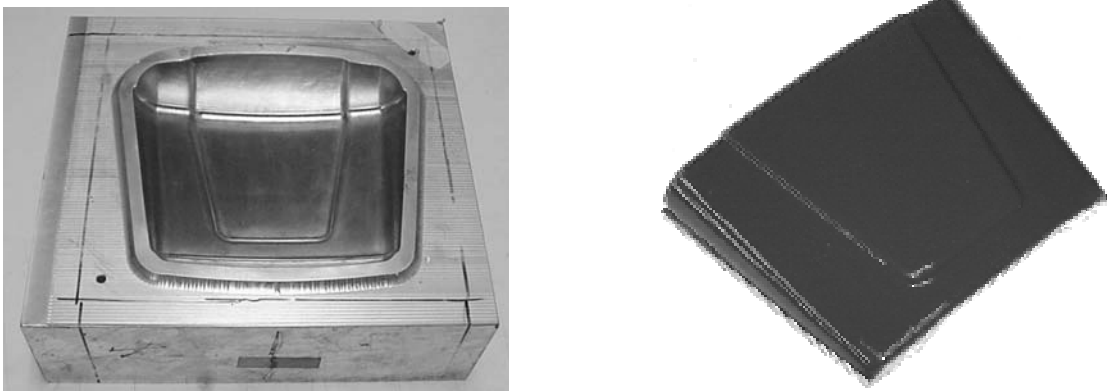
Molde usinado em alumínio e peça produzida pelo processo de moldagem por compressão.
